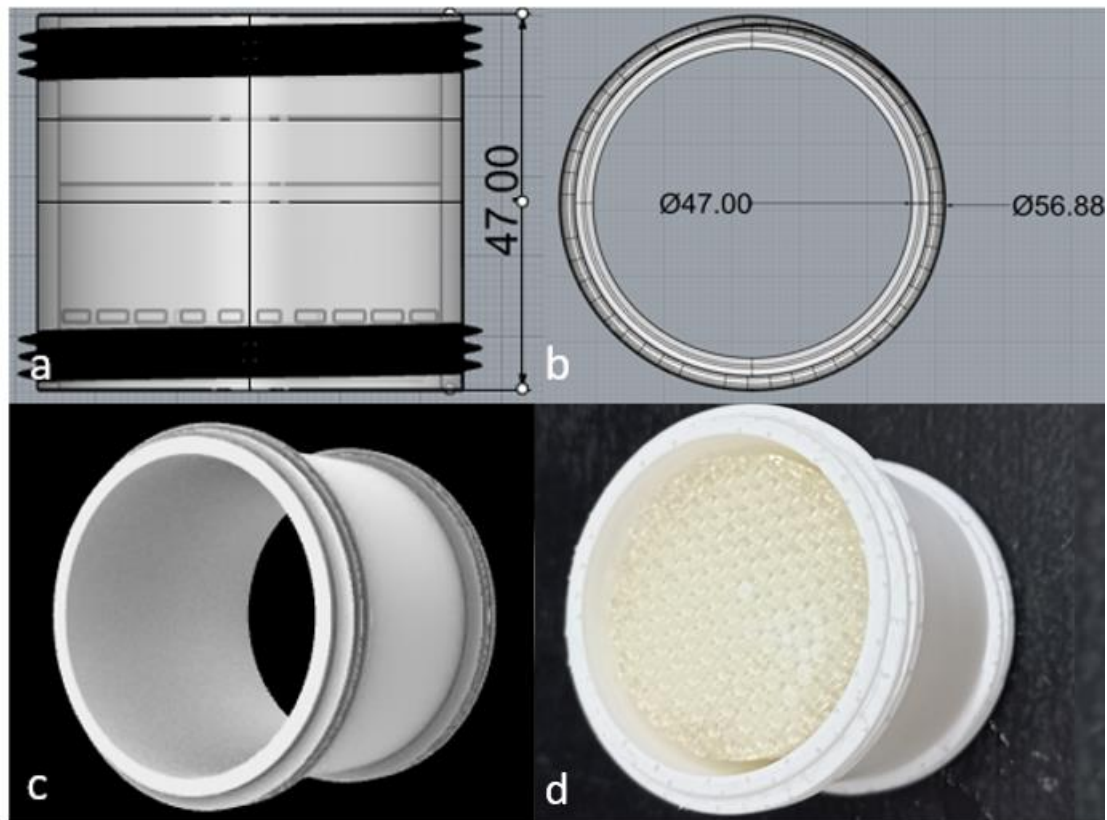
Tubería con rosca externa a: Vista frontal del dispositivo modelado en 3D; b: Vista superior del dispositivo; c: Vista en perspectiva; d: Fotografía de la impresión en 3D del dispositivo.
